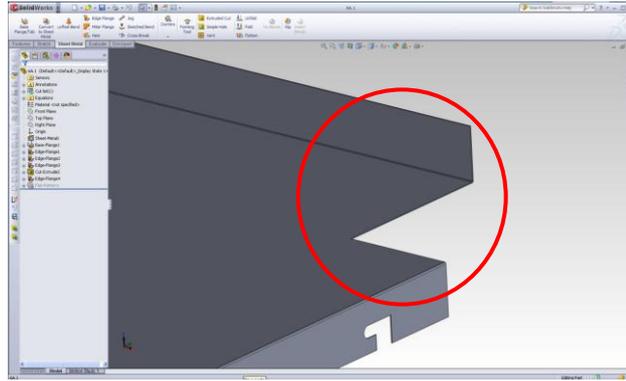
Encontro Painel e fachada na horizontal (Solidwork)
